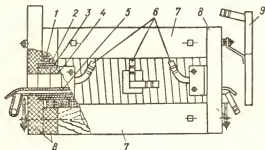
Индуктор для сквозного нагрева цилиндрических мерных заготовок;
